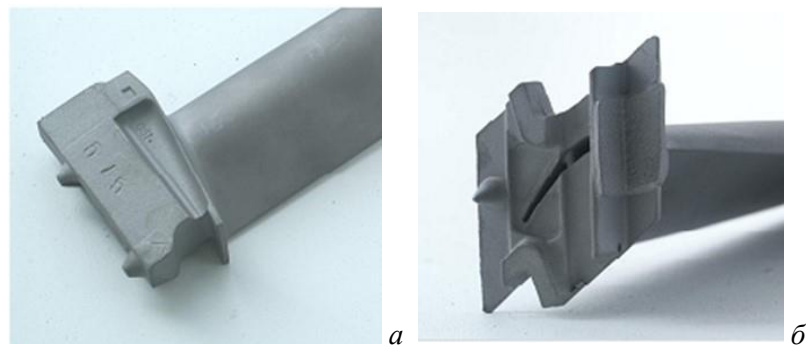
базові поверхні турбінної лопатки, виконані у виливку заготовки: а – з боку хвостовика; б – з боку бандажної полиці.
